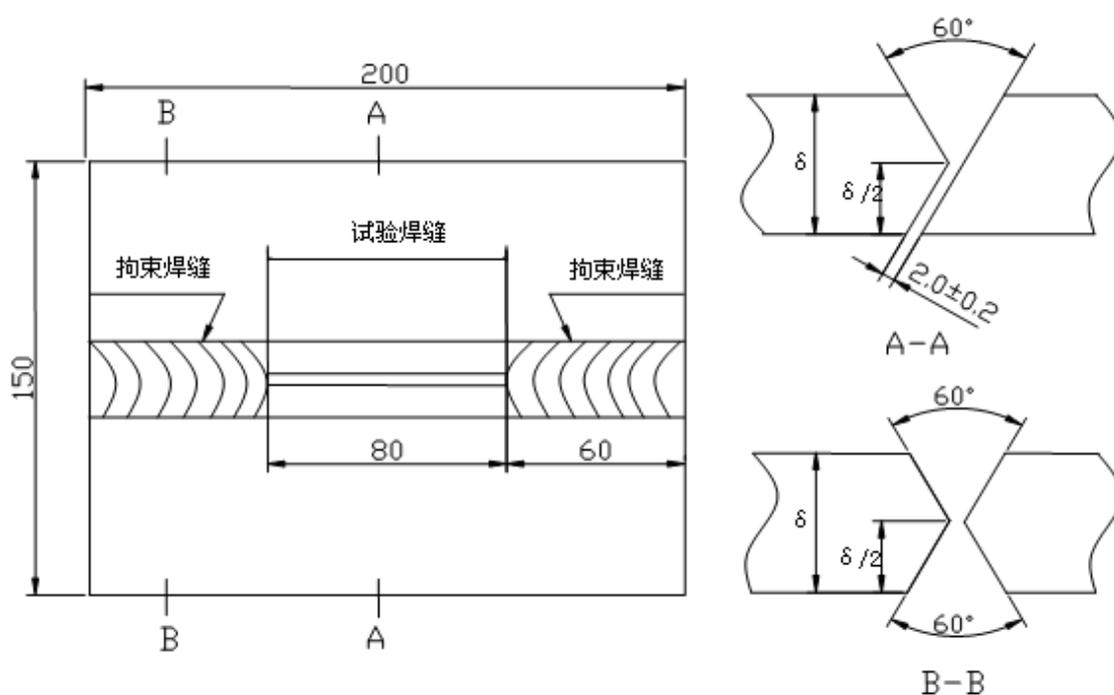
斜 Y 坡口焊接裂纹试件的形状和尺寸
